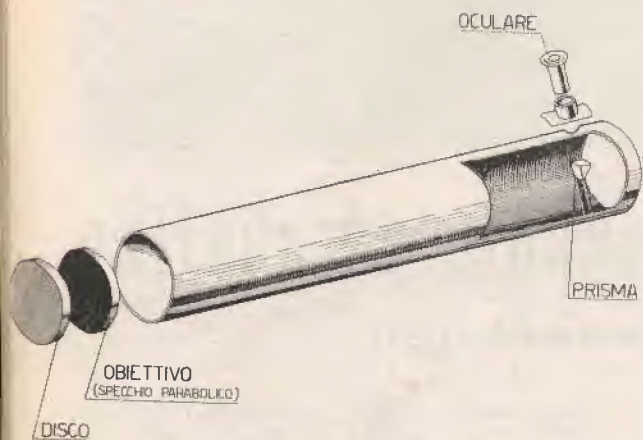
Schema montaggio parte ottica. - Sulla parte posteriore del tubo appare lo specchio parabolico montato sopra un disco di legno, il quale ultimo risulta solidale al tubo stesso mediante vite di presa laterale.
